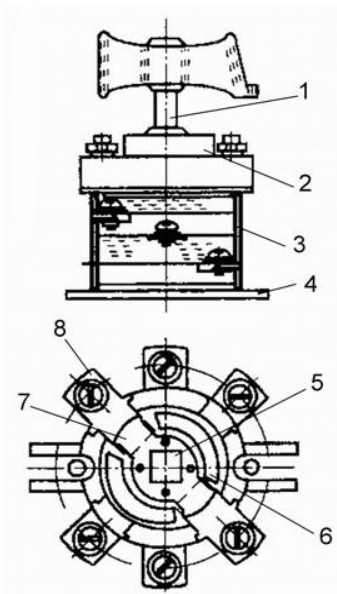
Конструкція пакетного вимикача: 1 – рукоятка; 2 – кришка; 3 – рульова тяга; 4 – кронштейн; 5 - профільний отвір; 6 – ізоляційний диск; 7 – рухомий контакт; 8 – нерухомий контакт
